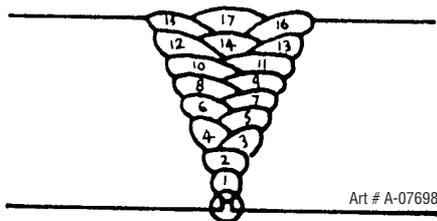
Séquence d'élaboration de la soudure
